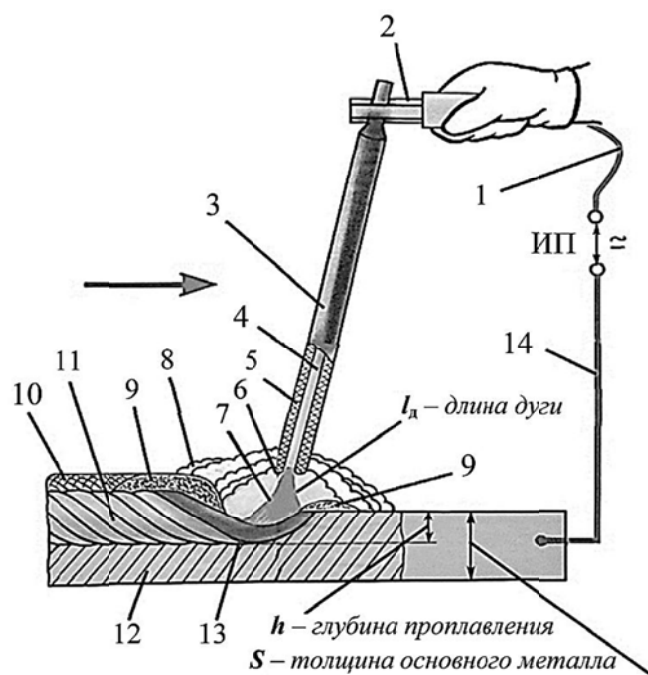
Схема процесса ручной дуговой сварки:
